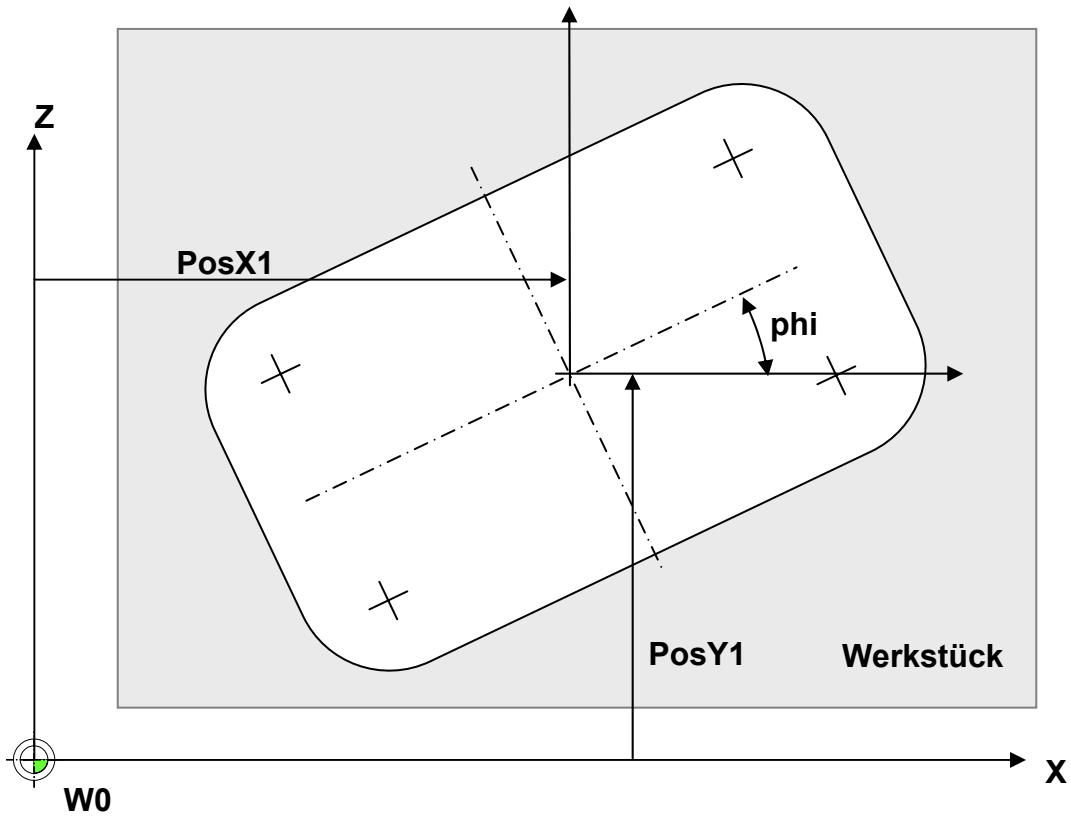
Parameter für die Definition einer rechteckigen Frästasche
